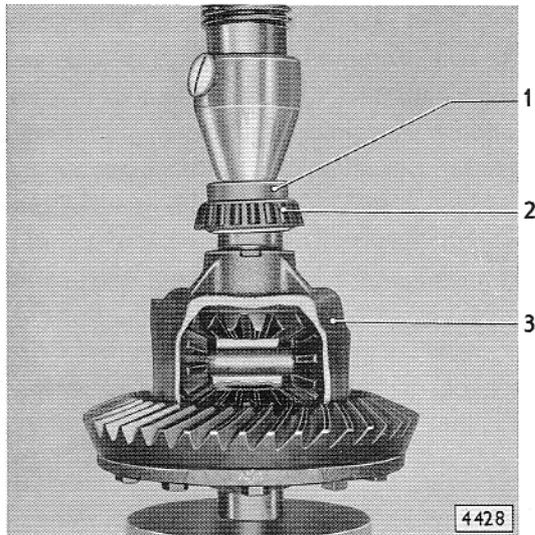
Rechtes Ausgleichgehäusekegellager aufpressen
